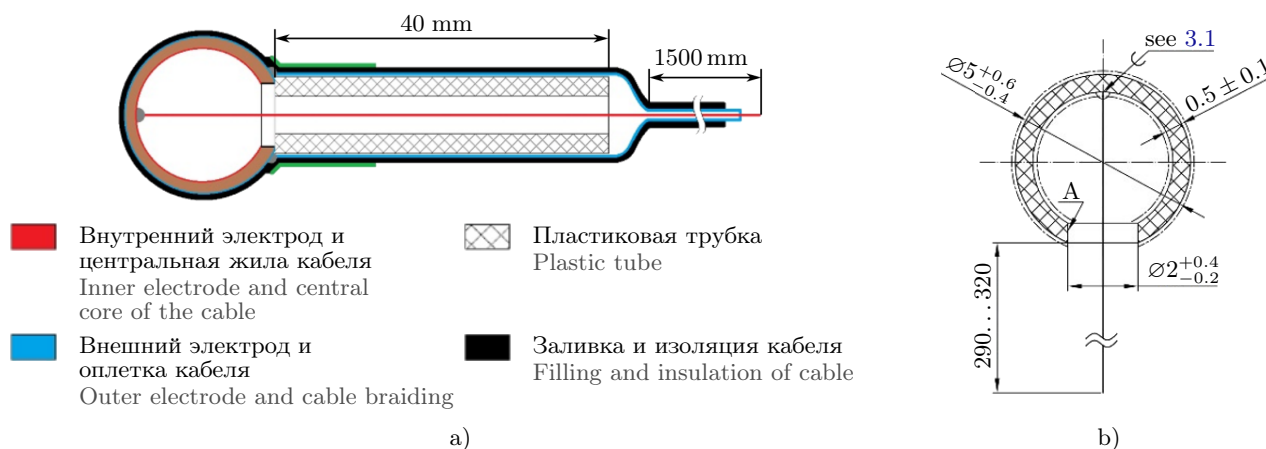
Устройство ультразвукового излучателя: а) источник излучения в разрезе; б) размеры пьезокерамической сферы
